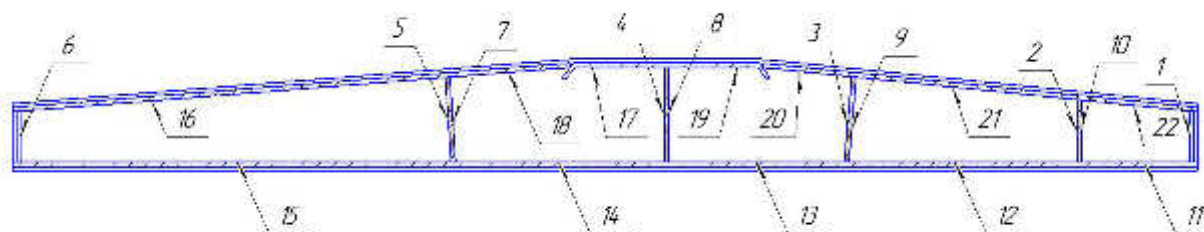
Порядок выполнения сварочных швов
